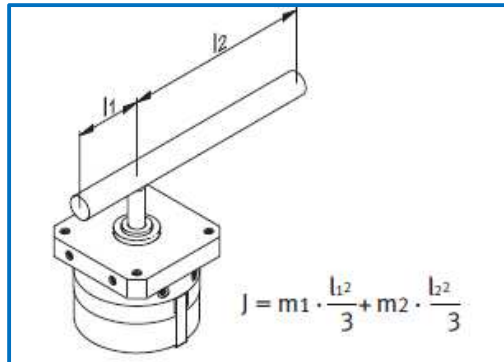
Eje delgado montado excéntricamente (posición horizontal)
